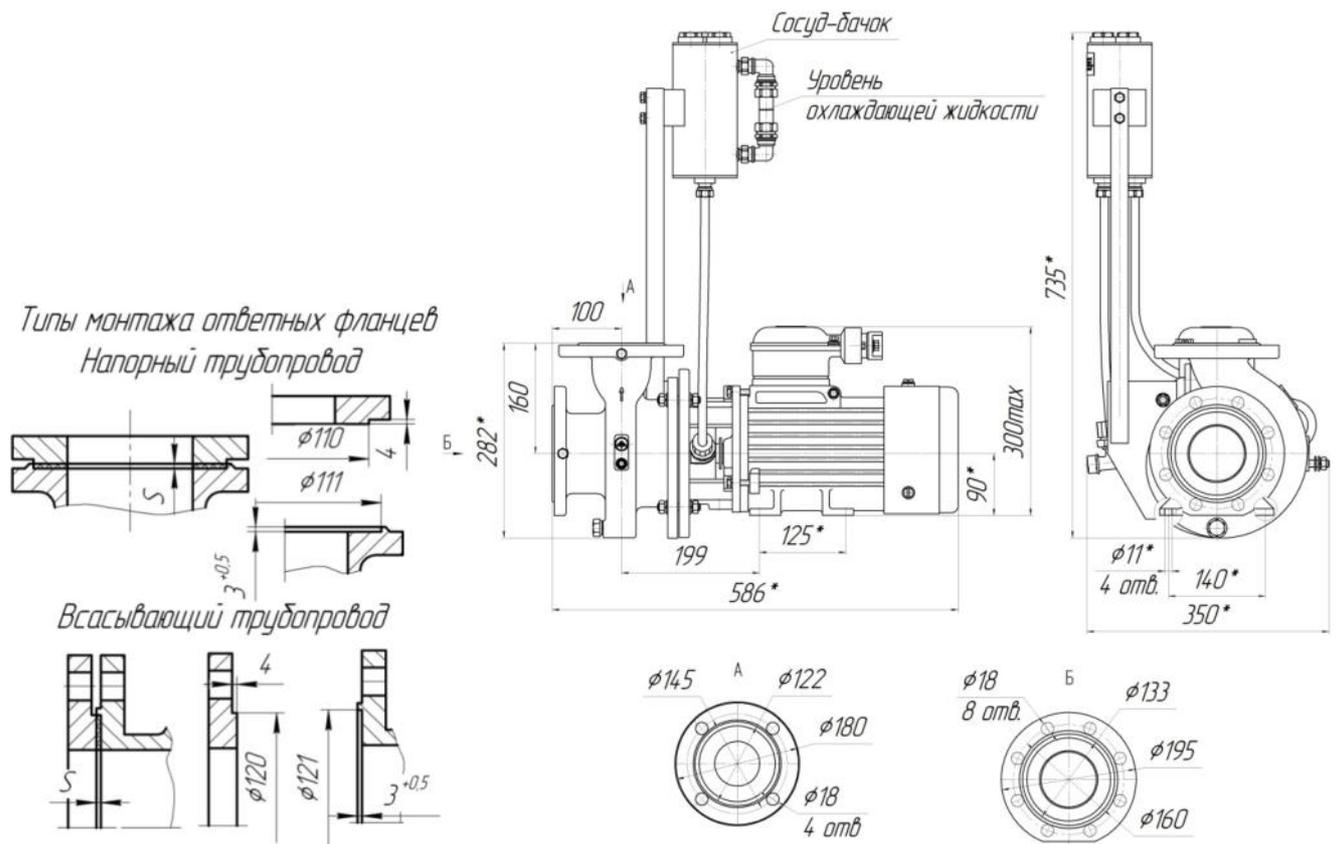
Габаритные и присоединительные размеры КМ 80-65-140Е-м с двойным торцовым уплотнением
